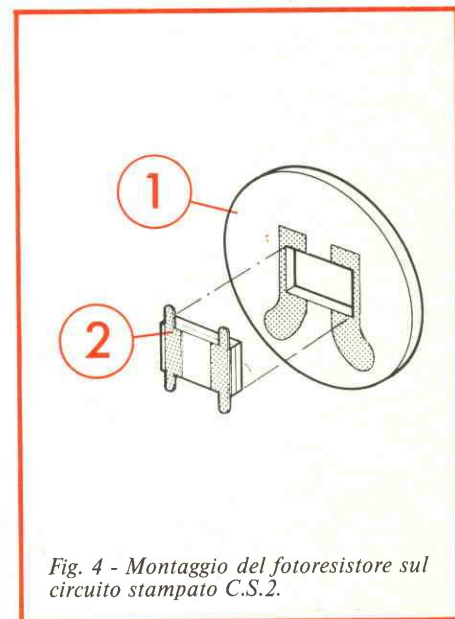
Montaggio del fotoresistore sul circuito stampato C.S.2.
